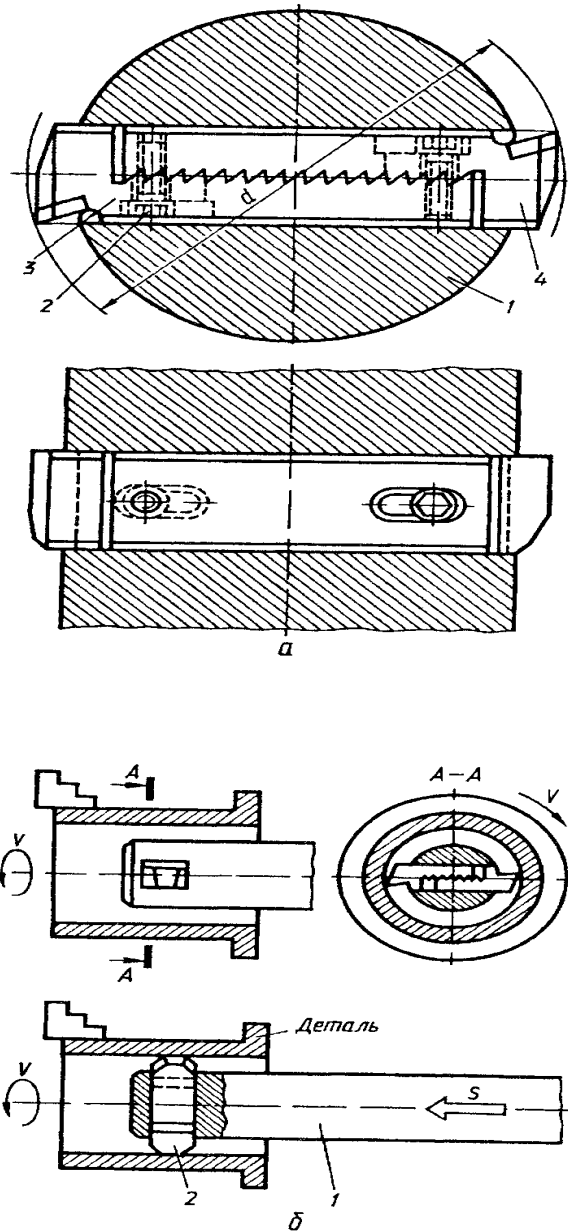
Плаваюча регульована розвертка: а - конструкція збірної плаваючої розвертки: 1 – оправка; 2 - нижня половина плаваючої пластини (А); 3 - верхня половина плаваючої пластини (Б); 4 – гвинт; б - схема застосування плаваючої регульованої розвертки: 1 - оправка, 2 - плаваюча розвертка
